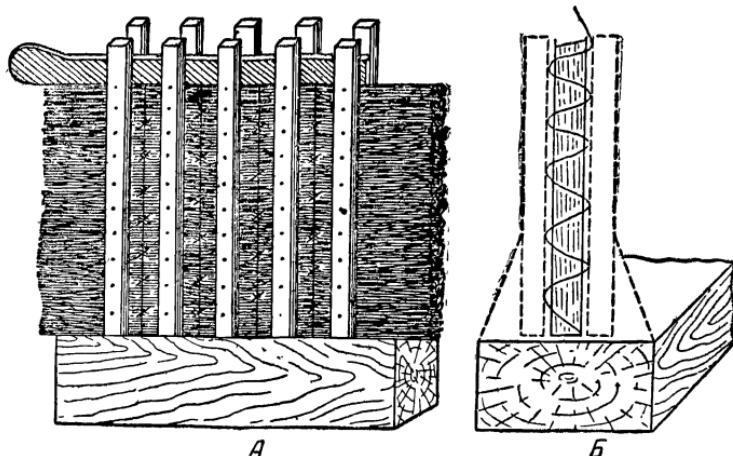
Станок для изготовления соломенных матов: *А* — общий вид станка с прессованной соломой; *Б* — поперечный разрез станка (способ сшивания мата).
